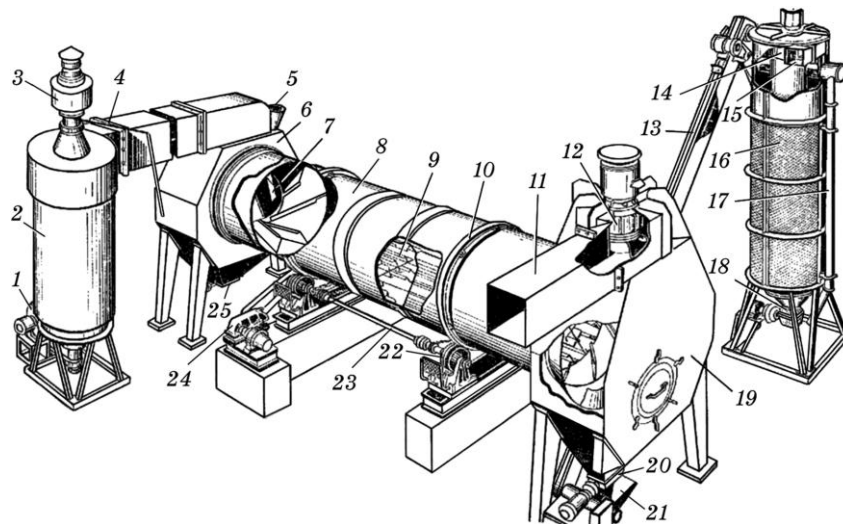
Загальний вигляд зерносушарки СЗСБ-8:
